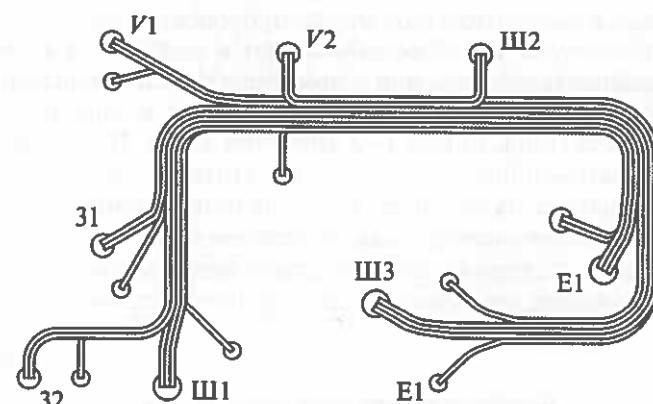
Плоский шаблон для раскладки монтажных проводов
